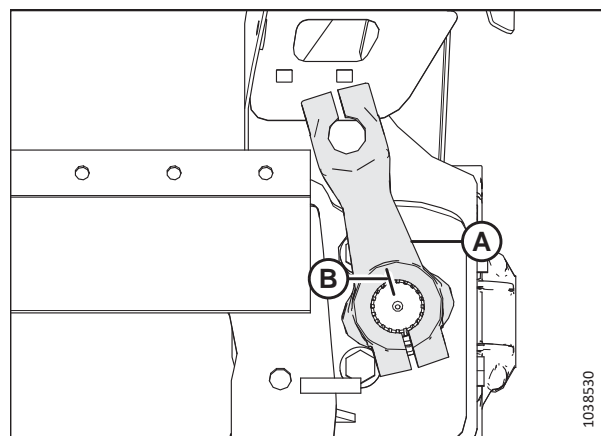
Приводной рычаг ножа — вид снизу
